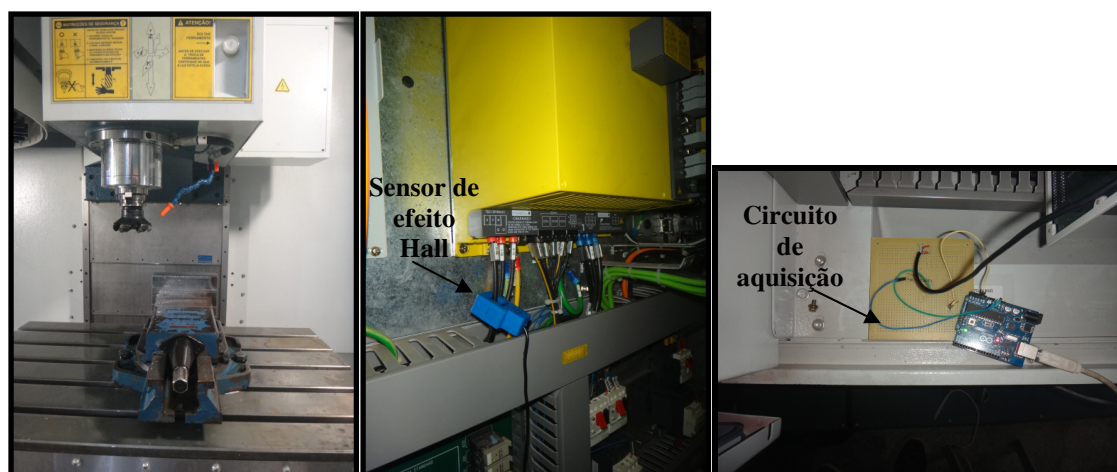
Arranjo de montagem dos ensaios de usinagem:
